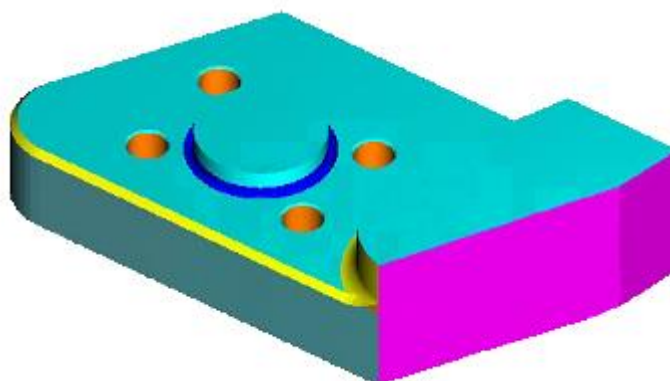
Stav obrobku po obrobení v operaci 080.
